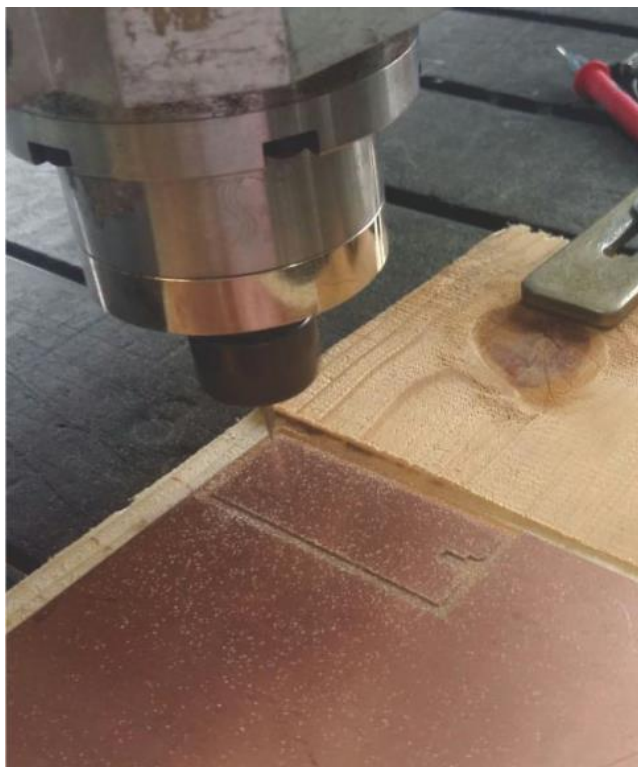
Usinagem do sensor pela Router CNC em placa de fenolite cobreada.
